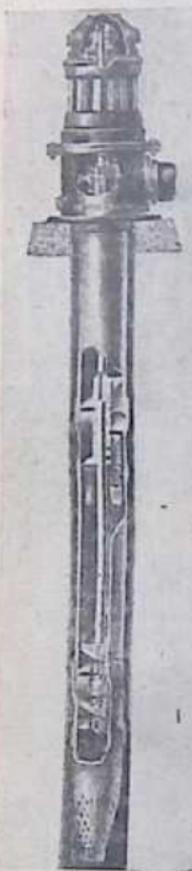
Разрез насоса прямого тока для глубоких колодцев, показывающий вал и колеса.
